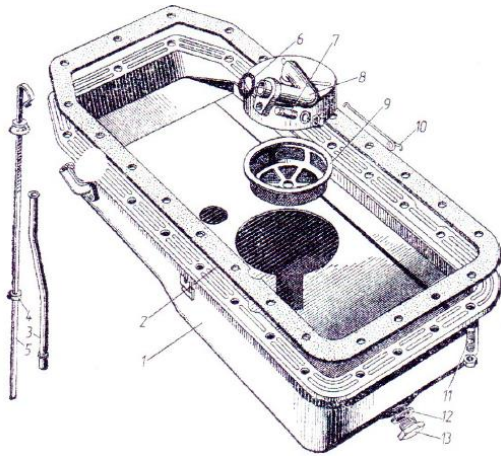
Оливний картер двигуна автомобіля: 11 - Шпилька М8х1х14 кріплення оливного картера - 23 шт.; Гайка М8х1 - 23 шт.
